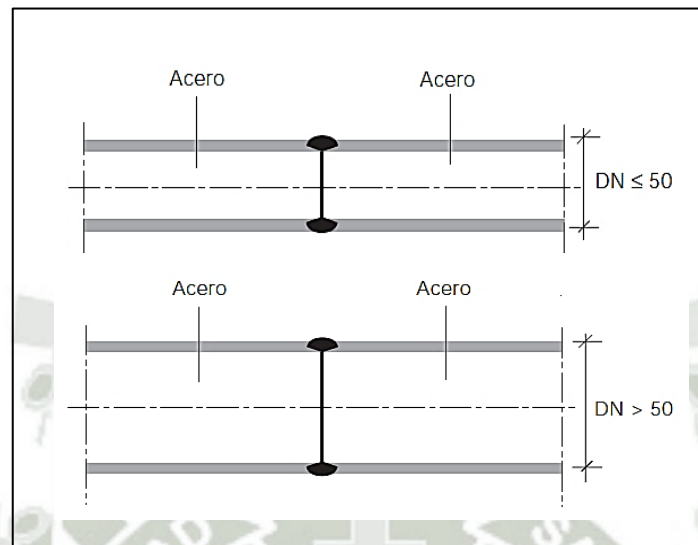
Soldadura eléctrica y oxiacetilénica para tuberías de acero.
